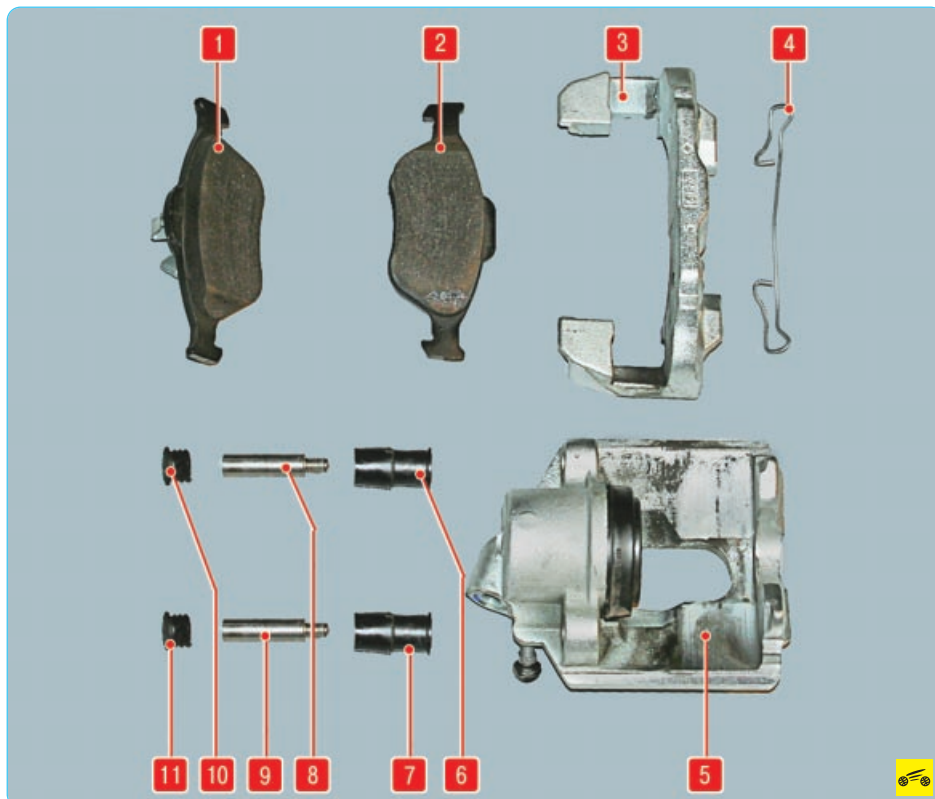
Детали тормозного механизма переднего колеса: 1 – внутренняя тормозная колодка; 2 – наружная тормозная колодка; 3 – направляющая колодок; 4 – пружинный фиксатор наружной колодки; 5 – суппорт; 6, 7 – защитные втулки; 8, 9 – направляющие пальцы; 10, 11 – крышки
